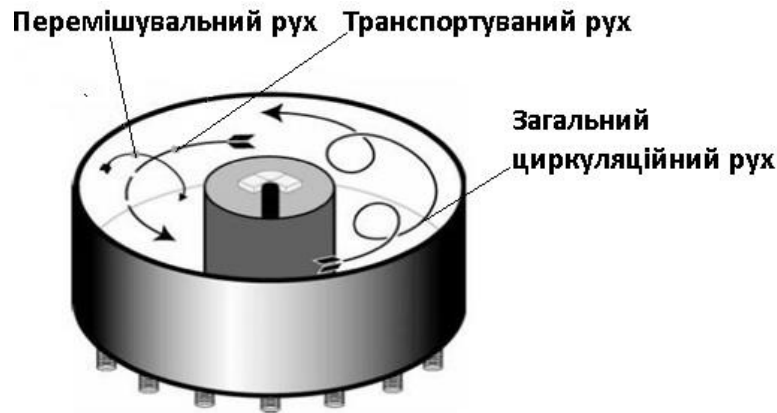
Схема руху частинок у камері кільцевої форми віброустановки
